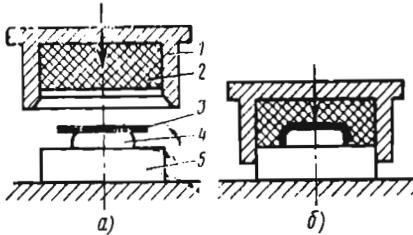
Схема оснастки для штамповки эластичной средой:
